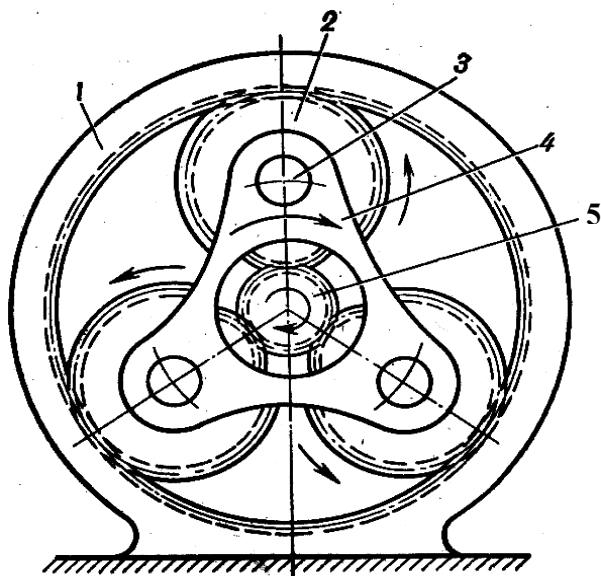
Схема планетарной зубчатой передачи ТД-1500:
